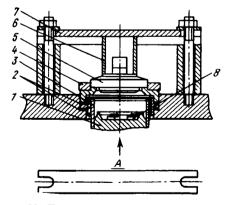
Приспособление для измерения величины линейного мертвого пространства: 1 — поршень; 2 — прокладки; 3 — гильза цилиндра; 4 — корпус всасывающего клапана; 5 — клапан нагнетательный; 6 — втулка; 7 — планка; 8 — свинцовые пластинки; 4 — эскиз планки
